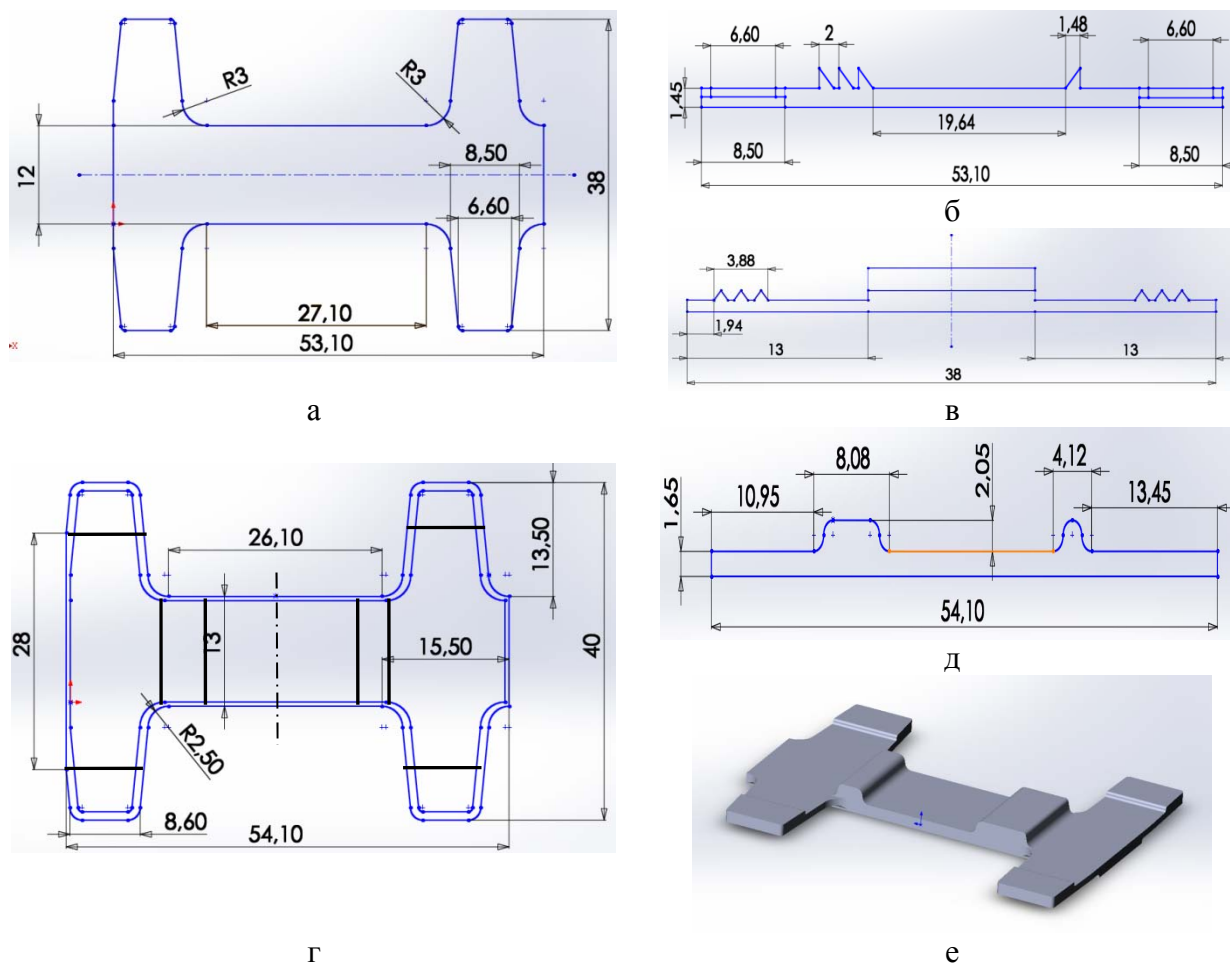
Развёртка детали (а–в) и поковки (г, д) с размерами:
